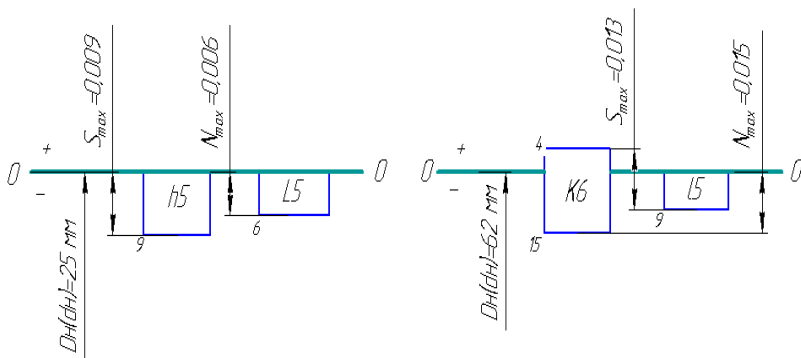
Схемы полей допусков сопряжений: внутреннее кольцо – вал, наружное кольцо – корпус
